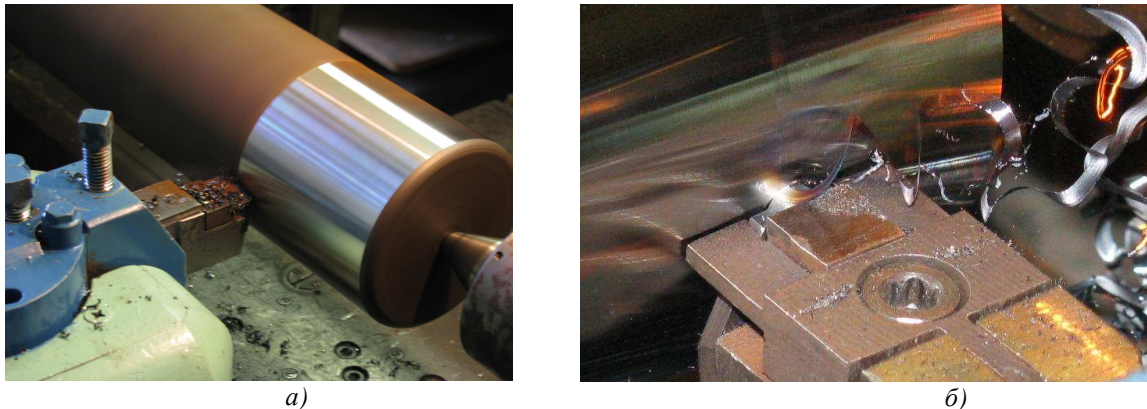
Точіння вала із загартованої сталі ШХ15 (HRC 62) різцем із циліндричною передньою поверхнею: а – чорнове точіння; б – чистове точіння
